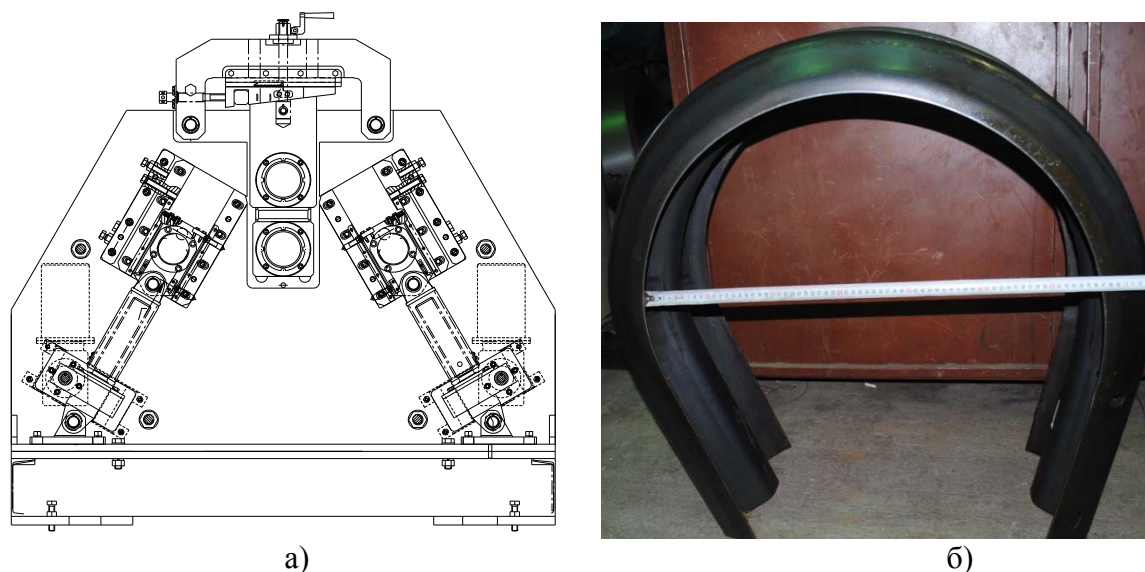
Машина гибочная: а – вид машины в разрезе; б – готовая деталь
